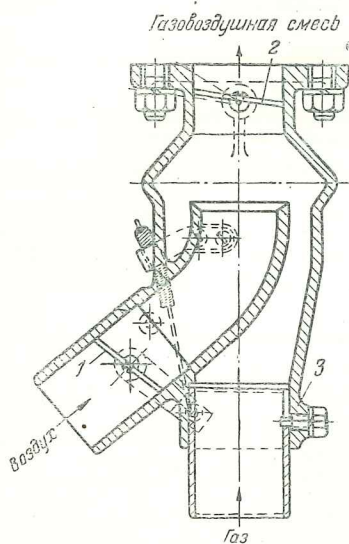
Схема смесителя установки ЗИС для автомобиля ЗИС-21
